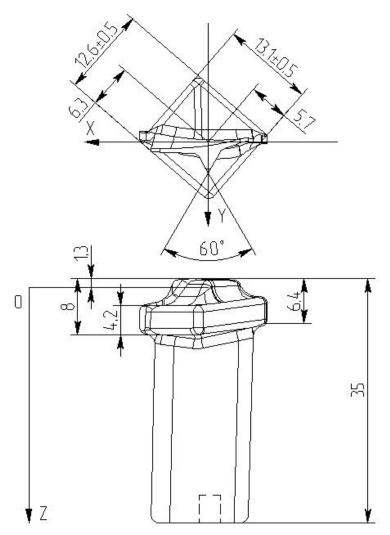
Эскиз поковки лопатки 7 ступени двигателя ВК-2500
